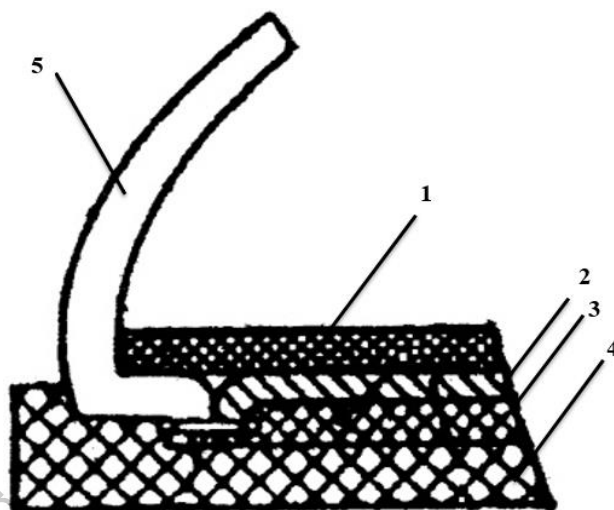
Схема сечения обуви строчно-литьевого метода крепления: 1 – вкладная стелька; 2 – втачная стелька; 3 – простилка; 4 – подошва; 5 – заготовка
